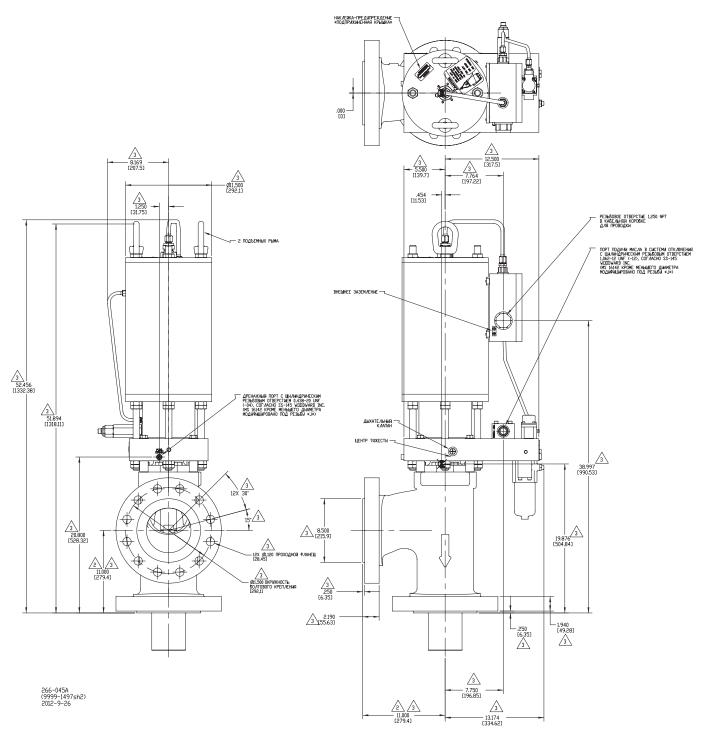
а. Габаритный чертеж регулятора SonicFlo (6 дюймов, класс 600)
